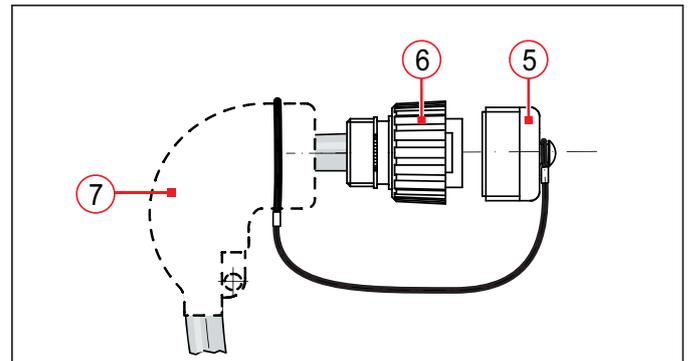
Beispiel für Stecker mit Gewinde und 90° Formschrumpfteil (gilt analog auch für Dosen mit Gewinde)
